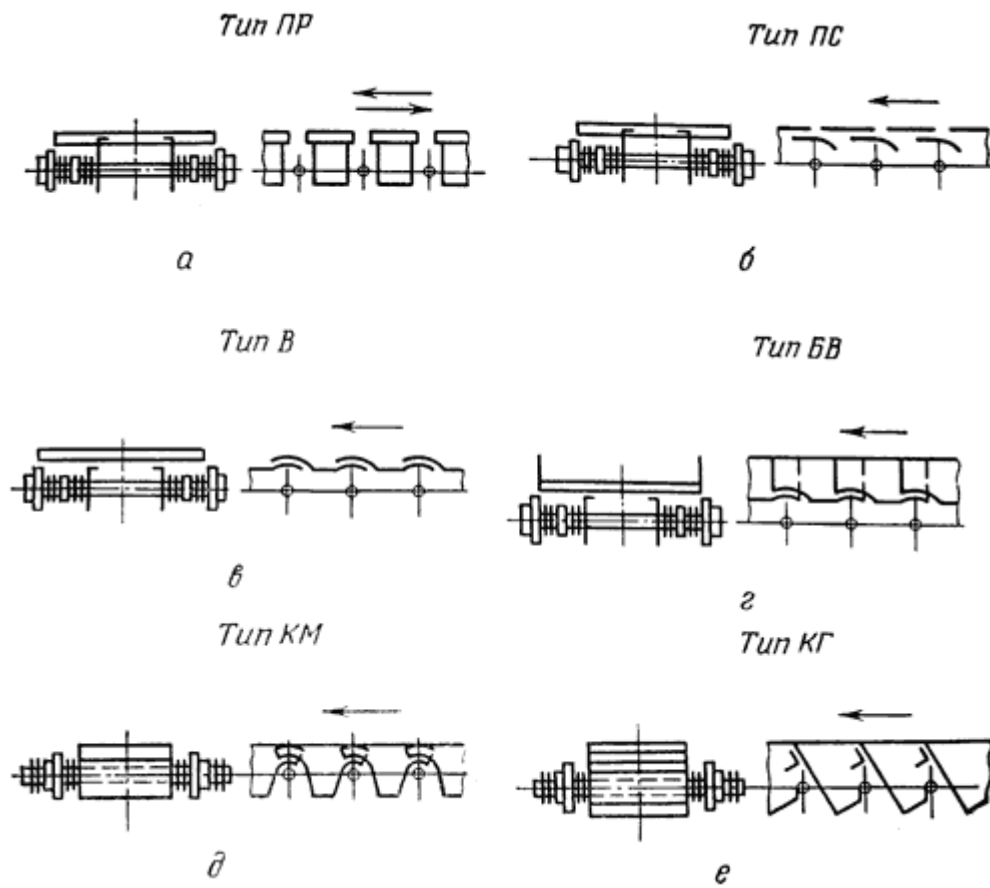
Основні типи пластинчастих конвеєрів: а – плоский розімкнений; б – плоский замкнутий; в – безбортової хвилястий; г – бортовий хвилястий; д – коробчатий дрібний; е – коробчатий глибокий.
